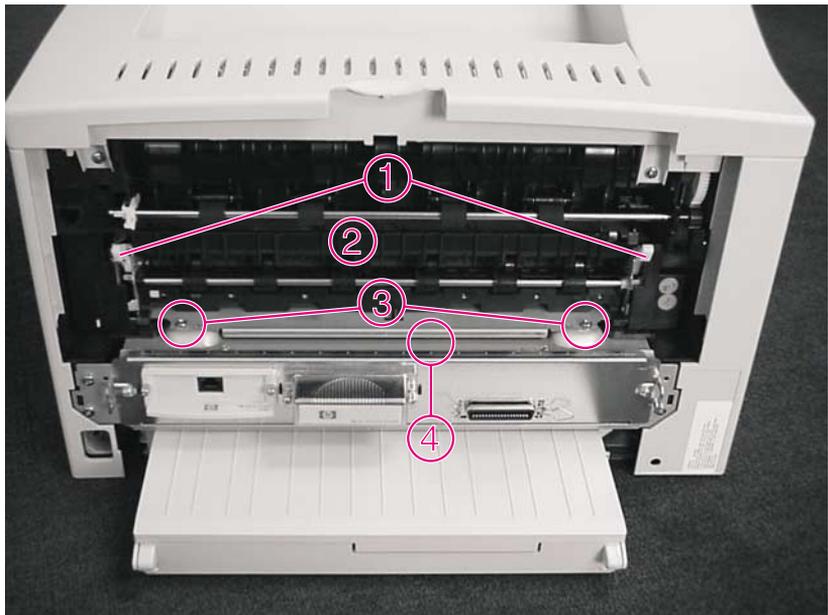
Entfernen der Fixiereinheit (Rückansicht des Druckers)
